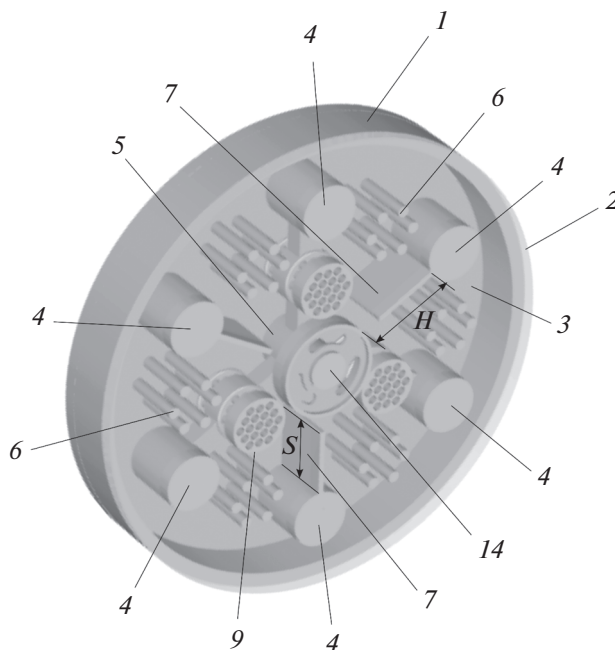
Конструкция резонатора: 1 – цилиндрический корпус; 2, 3 – боковые крышки резонатора; 4 – боковые опорные стержни; 5 – центральный опорный стержень; 6 – металлические стержни; 7 – радиальные перегородки (ребра); 9 – боковые пролетные трубы; 14 – центральный проводник коаксиального вывода энергии.
